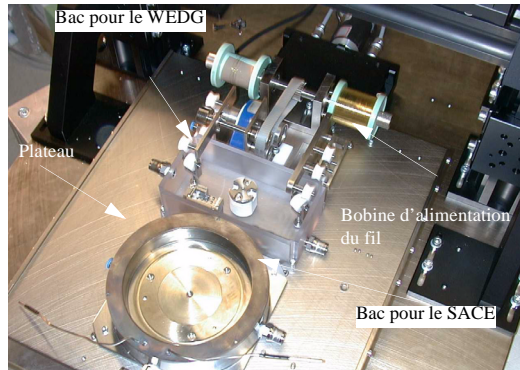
Photographie du plateau et des deux unités d'usinage (SACE et WEDG).
